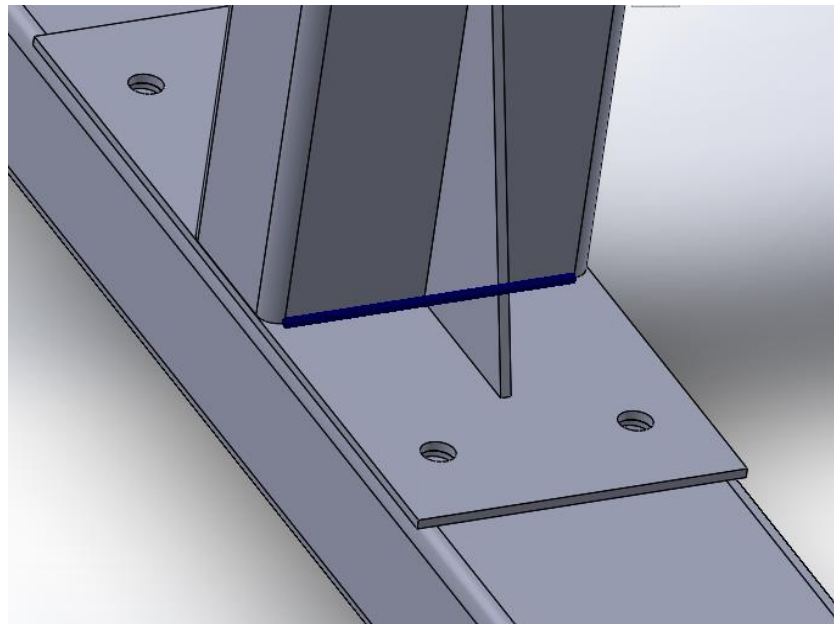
Esquema de soldadura entre la placa base y la columna.
